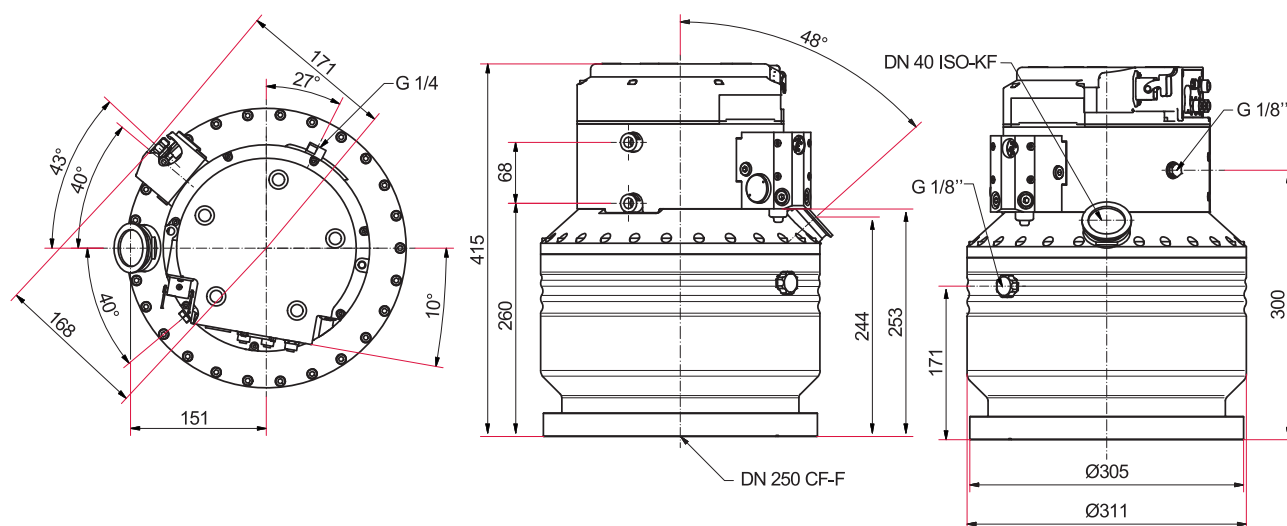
Dimensions HiPace 2300 U et HiPace 2300 UC | DN 250 CF-F
